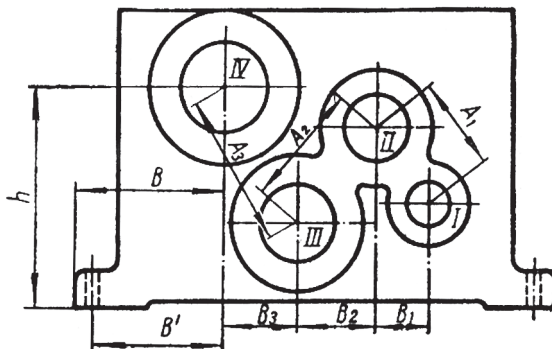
Корпус для свернутой компоновки 3-ступенчатого редуктора
